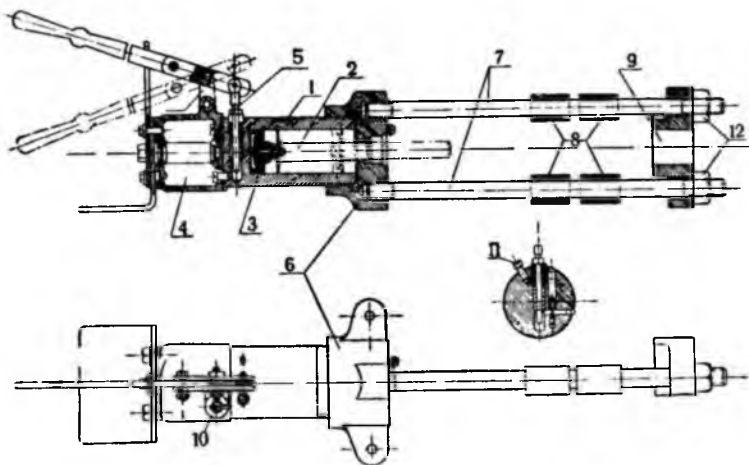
Переносный гидравлический пресс с ручным приводом для перепрессовки гусениц:
